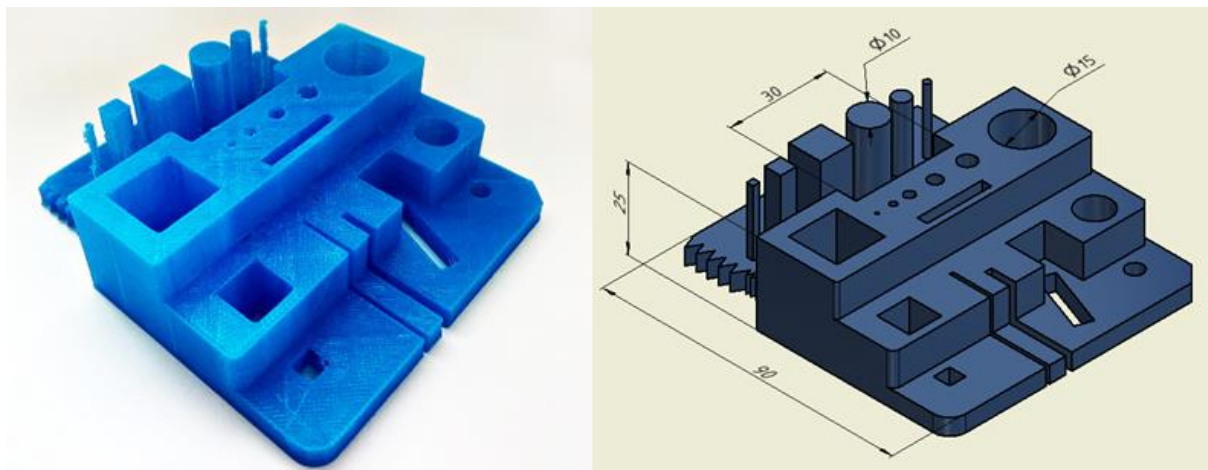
Напечатанная деталь и контролируемые размеры после печати
